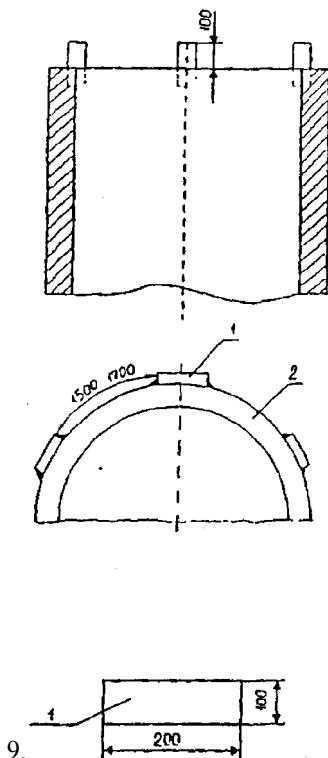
Установка монтажных планок на обечайку: 1 – монтажная планка;
